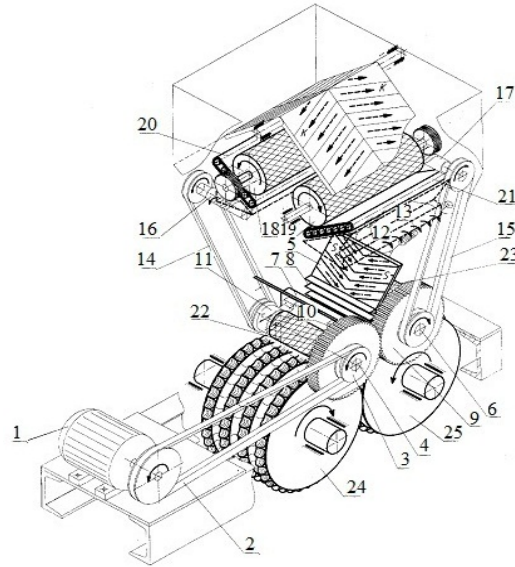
Конструктивно-технологическое исполнение ПВА с устройствами для предварительного уплотнения шихты и их кинематические схемы привода:
